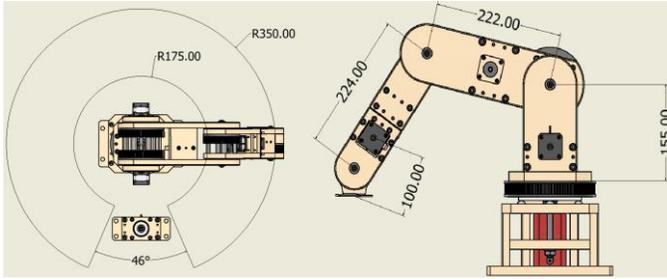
Dimensiones generales del diseño, Fuente: Autor
